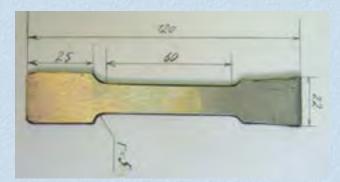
Образец для испытаний на растяжение из сплава, выплавленного из руды Ленского рудного поля, в частности, из рудопроявления «Куртанг»
